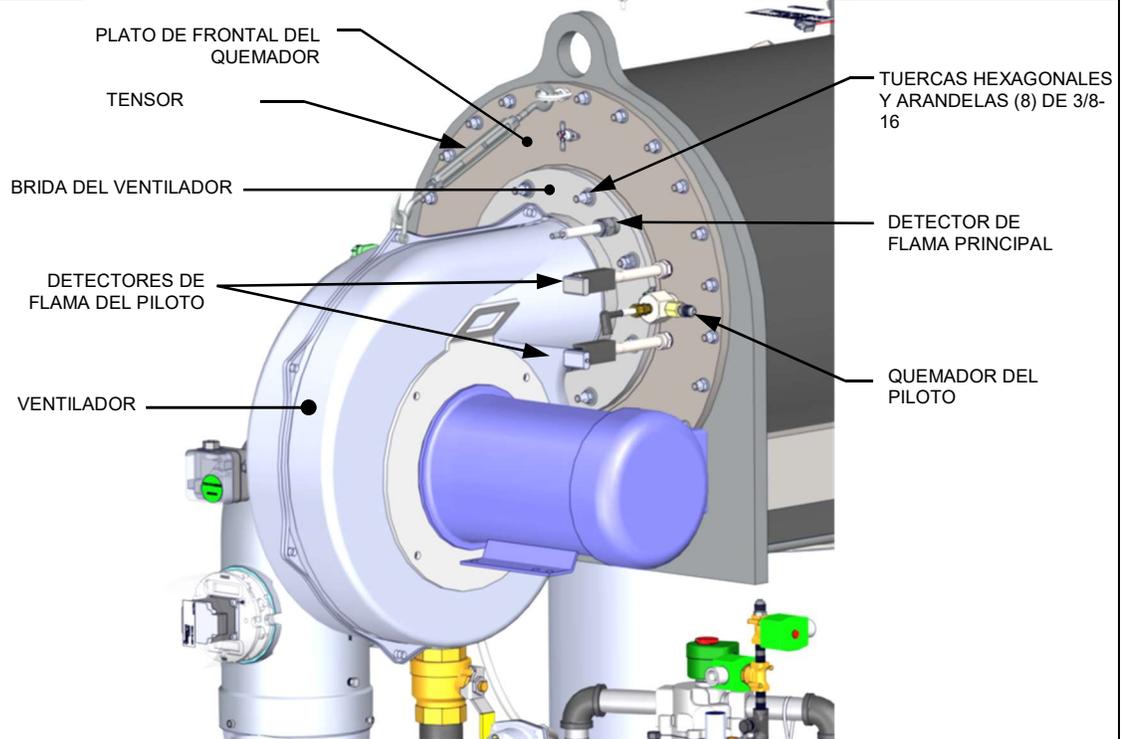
Detalles del montaje del ensamblado del quemador - Vista frontal derecha
